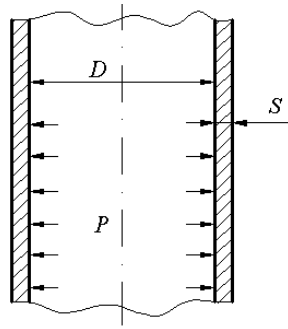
Схема циліндричної обичайки корпусу апарата
